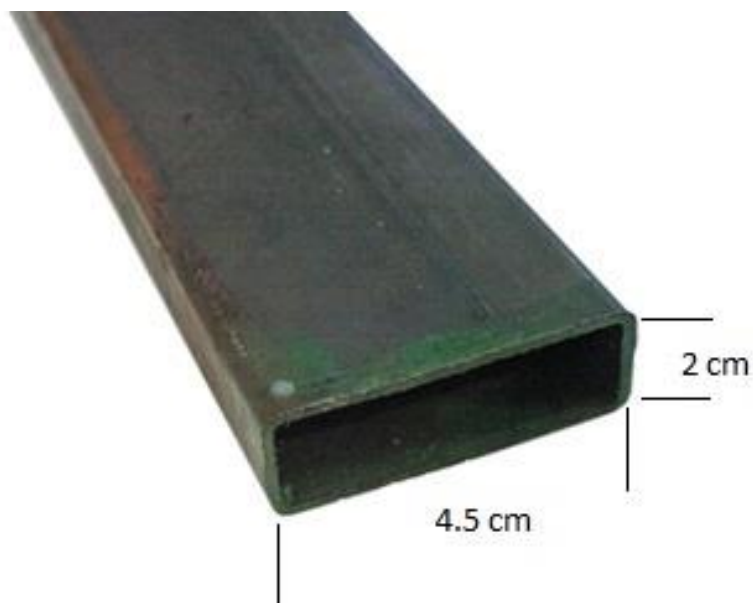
Tubo de Acero para el armado de la estructura de la banda
